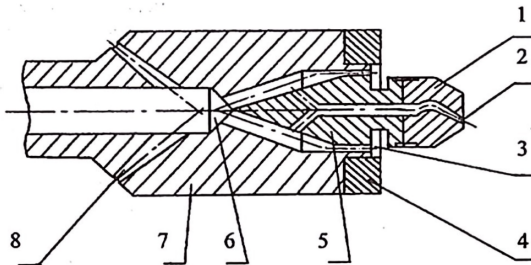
Схема гідроакустичної дренопровимної головки. 1 - фронтальна насадка; 2 - фронтальне сопло; 3 - кавітаційна порожнина; 4 - кільцева насадка; 5 - обтічак; 6 - центральний канал; 7 - корпус; 8 - реактивні сопла.
